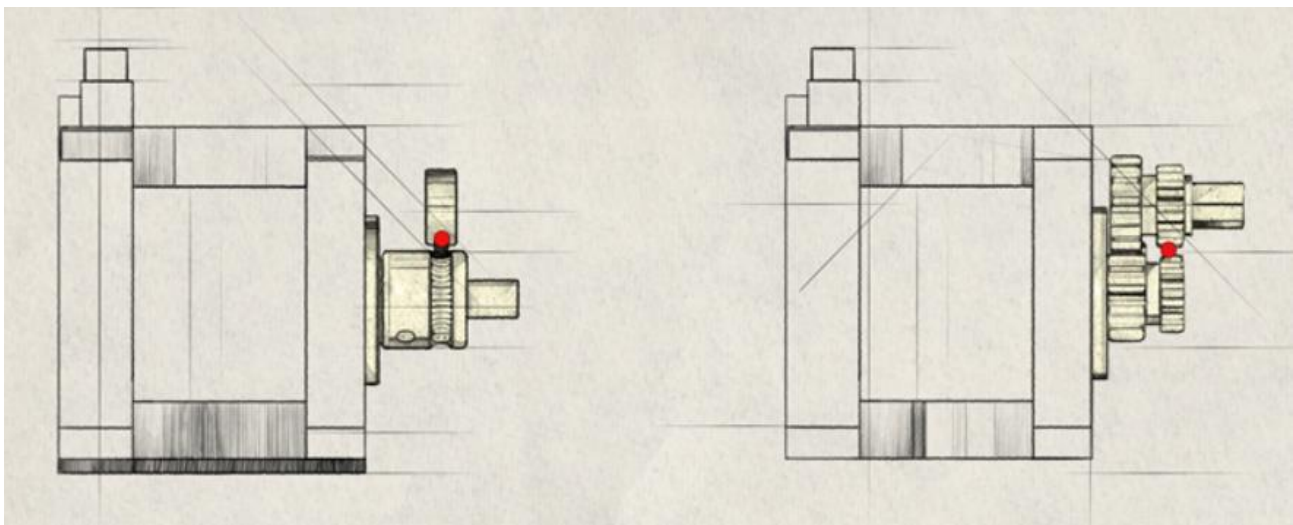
Distribución de fuerzas. Engranaje-Engranaje.
